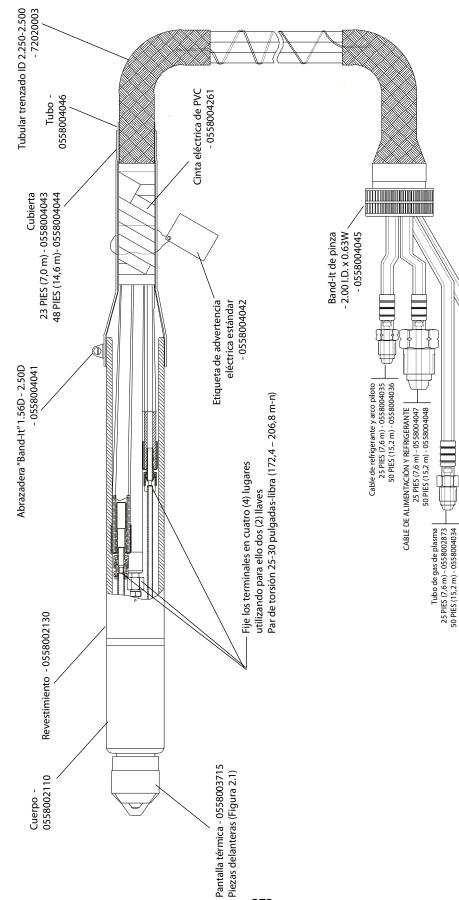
Piezas de recambio - Montaje de soplete PT26 In-Line
